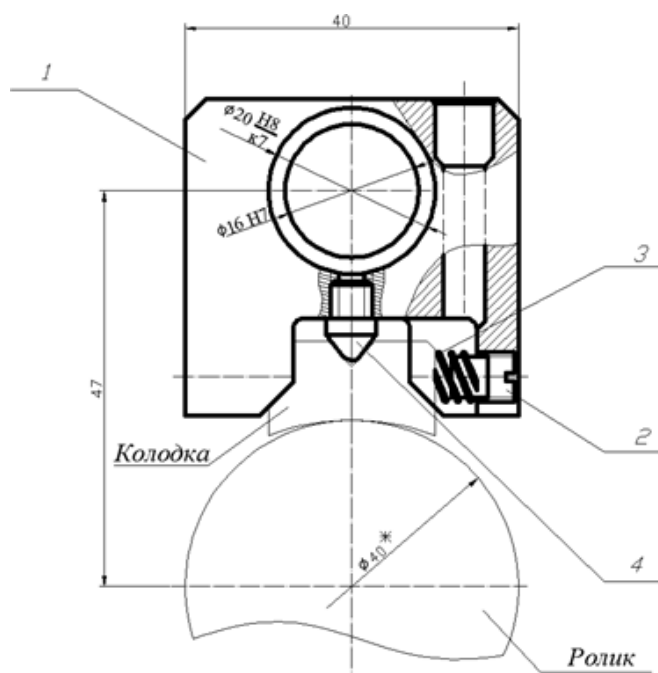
Разработанная конструкция держателя: 1 – пластина; 2 – винт; 3 – пружина; 4 – конус
